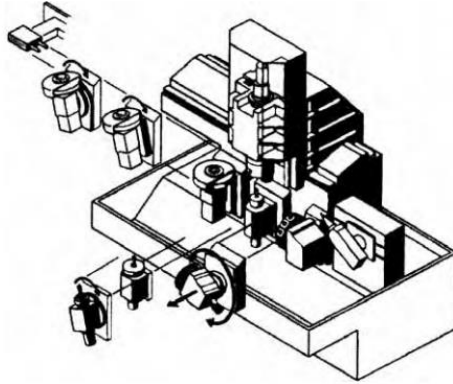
Токарно-шліфувальний багатоцільовий верстат модульної конструкції фірми Index-Werke GmbH & Co.KG
